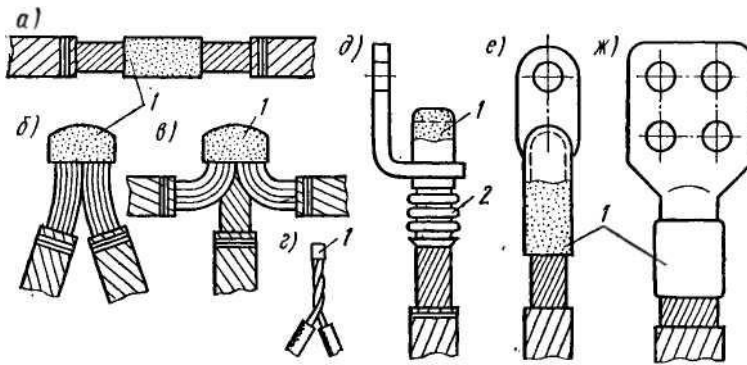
Виды соединений и окончаний кабелей и проводов с алюминиевыми жилами, выполняемых термитно-муфельной сваркой;
